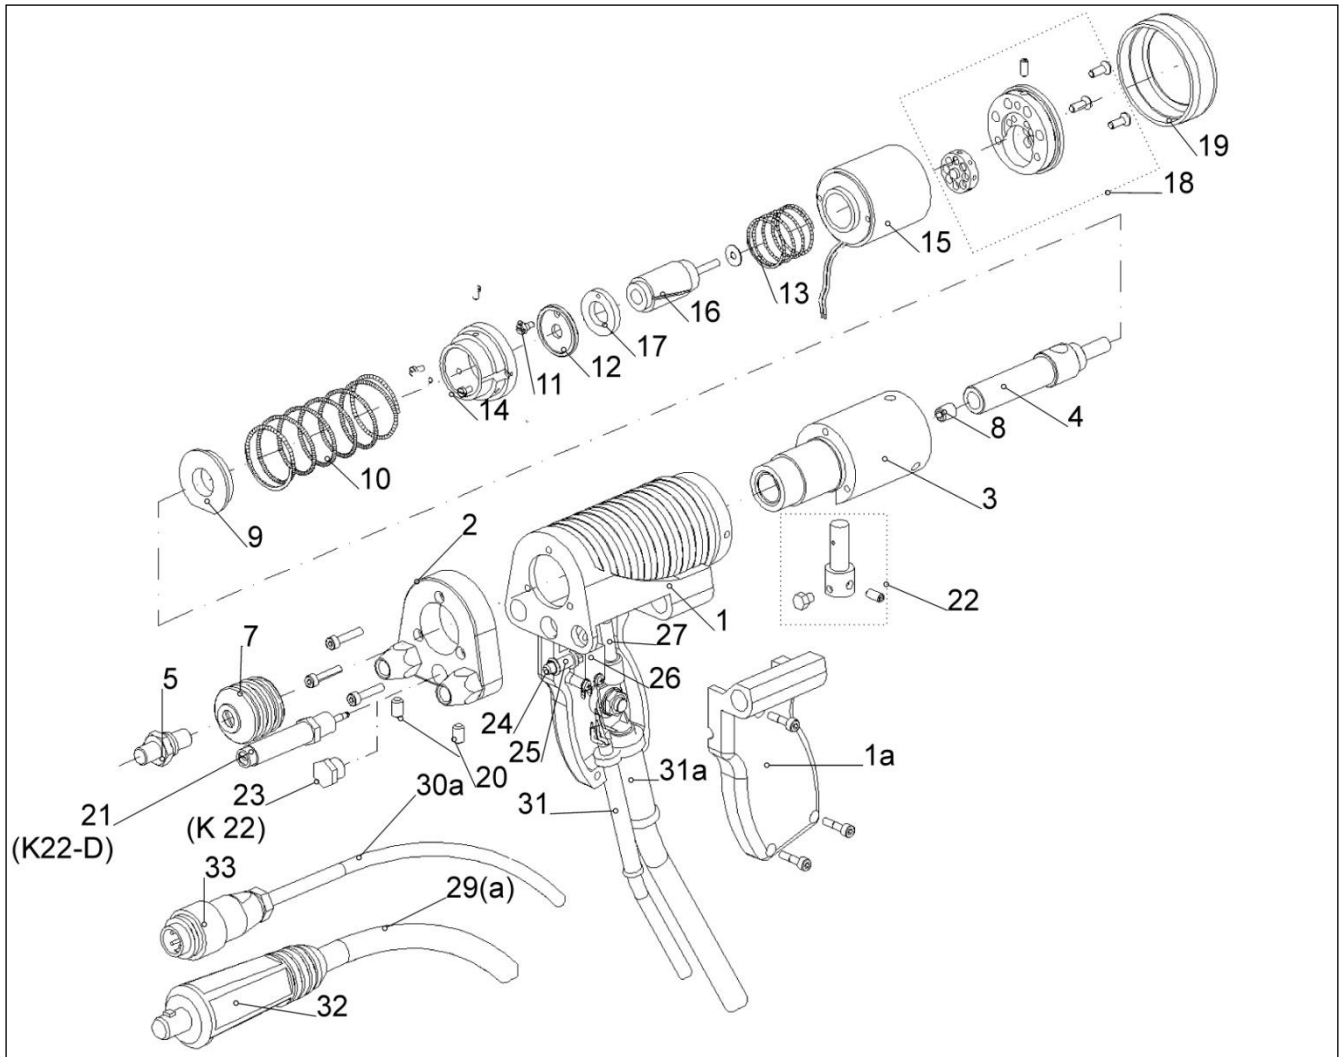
Detailansicht der Pistole K 22 mit Option K 22-D
